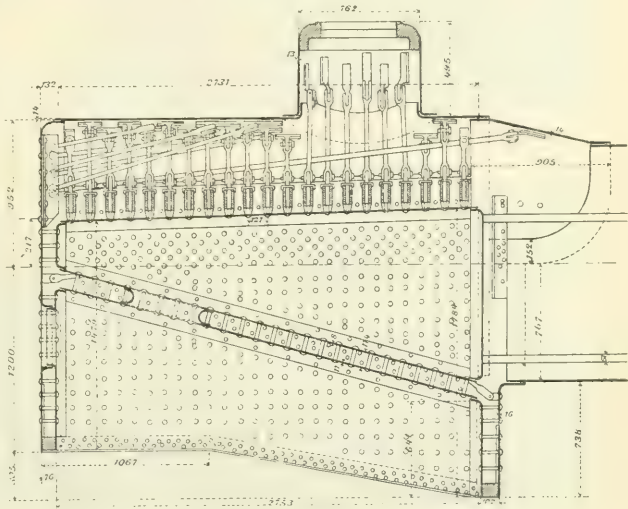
Stehkessel mit Wasserkammer, Bauart Buchanan.
